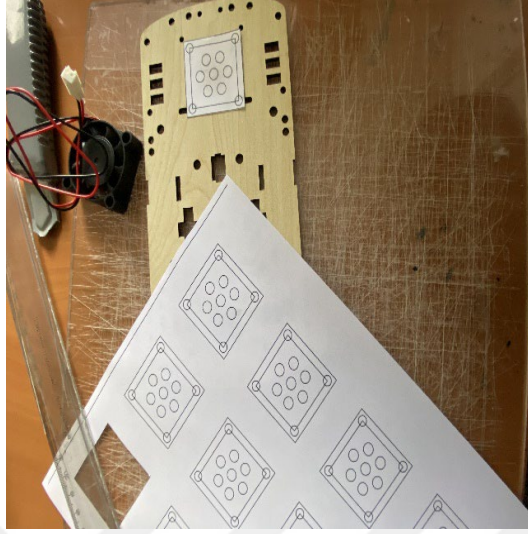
28 BYJ-48 step motor montajının yapılması.
